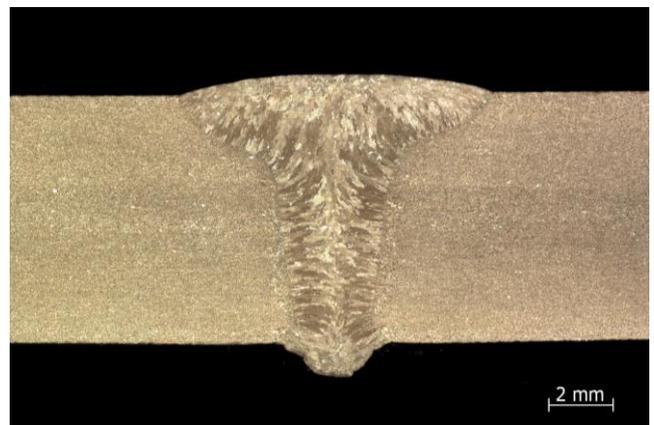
Plasmastichloch geschweißt, Schliffbild
